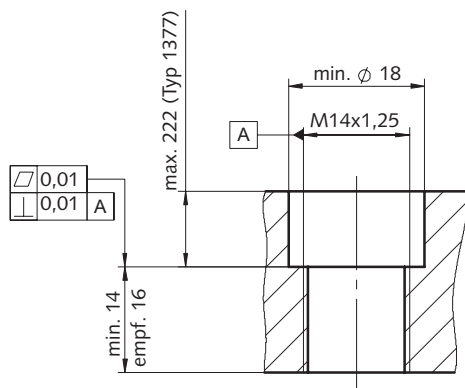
Bündig eingebauter Sensor. Bohrungsdurchmesser gemäß Montagewerkzeug
